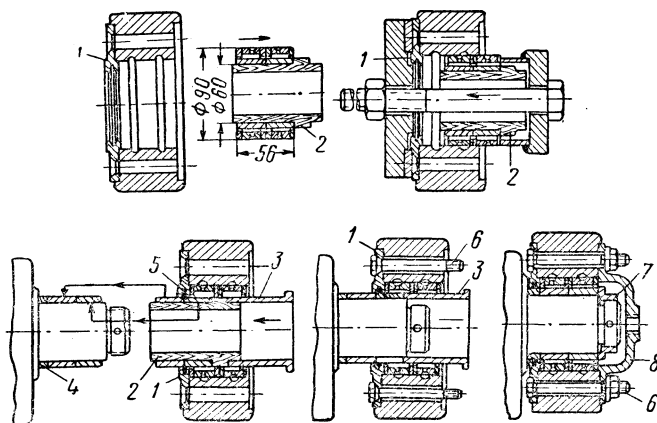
Схема разборки игольчатых подшипников цапф кулисы:
